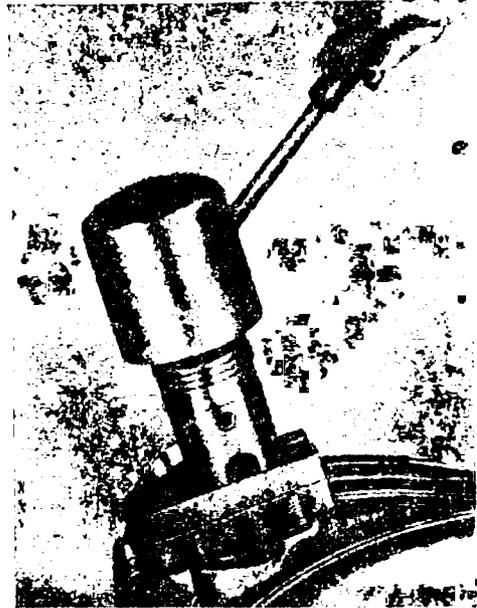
Anwärmen des Kolbens mittels Wärmekappe, die vorher im Schmiedefeuer oder mittels Schweißbrenner angewärmt wurde
